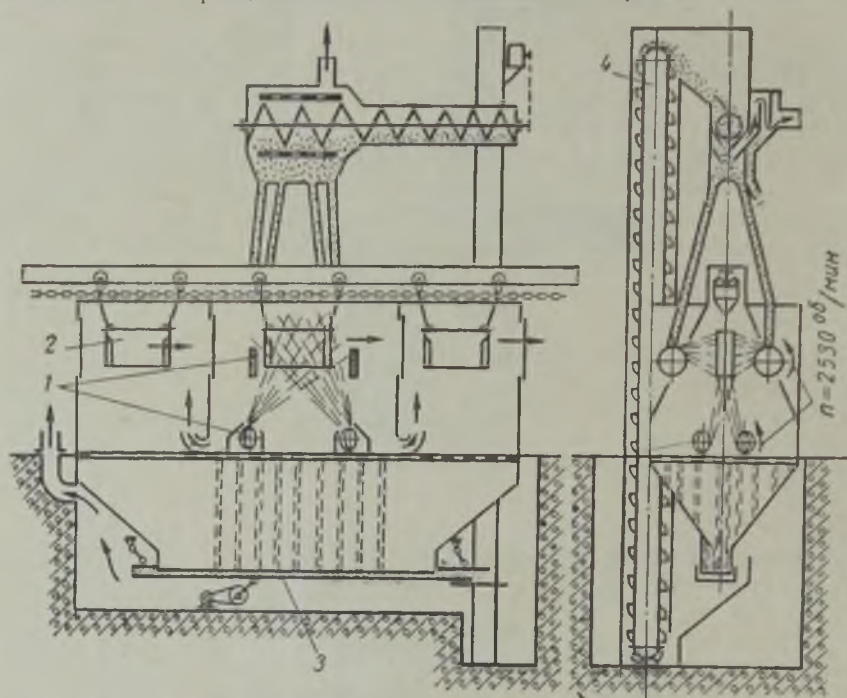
Схема шеститурбинной дробебетной установки для очистки крупных отливок:
